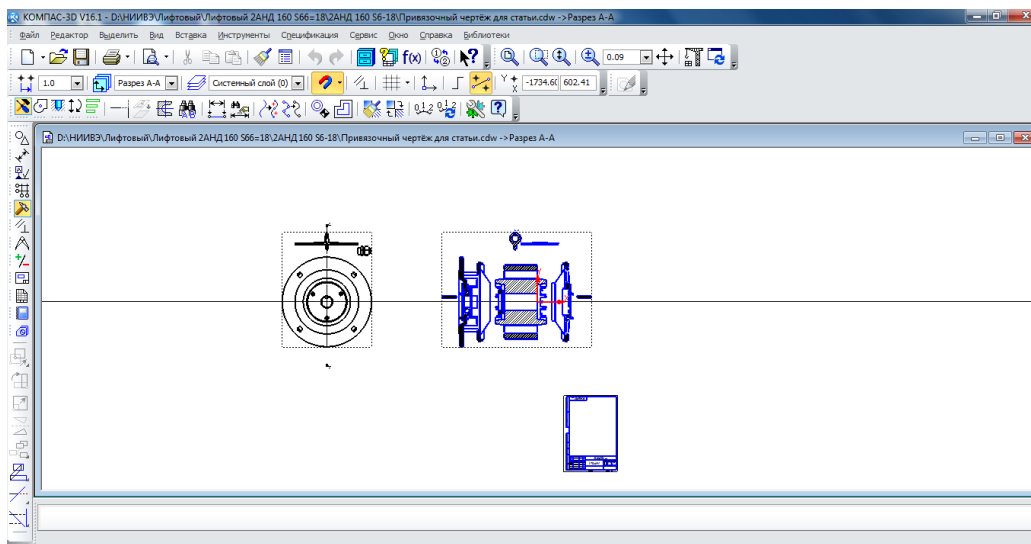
Привязочный чертёж каркаса электродвигателя 2АНД 160 S6/180
